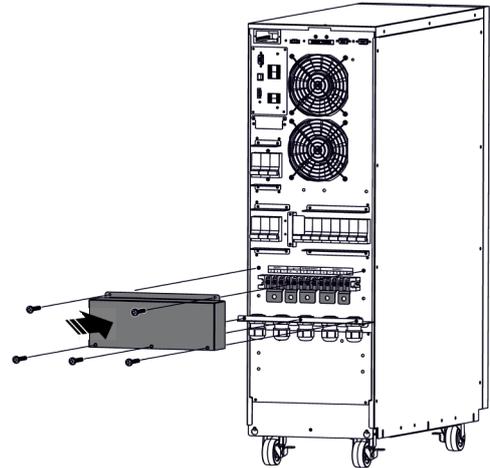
Re-ubicación de la cubierta de protección de los terminales de conexión.
